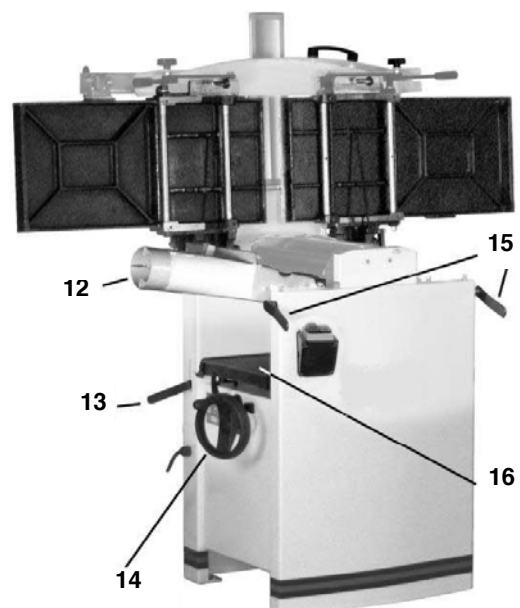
Abricht- und Dickenhobelmaschine ADH 26 C
